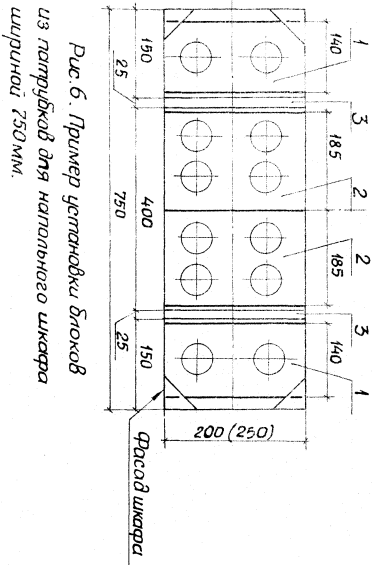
Пример установки блоков из патрубков для напольного шкафа шириной 750 мм.
